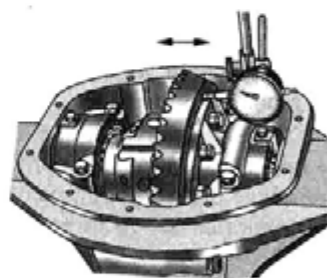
Проверка осевого зазора в подшипниках дифференциала (неразъемный задний мост)
